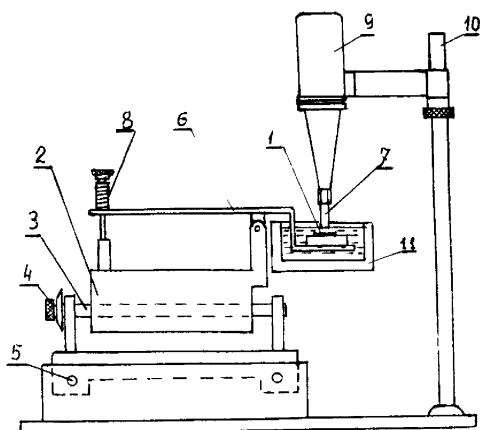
Схема устройства для поверхностной ультразвуковой обработки: 1-образец; 2-каретка; 3,5- направляющие для перемещения образца в двух взаимно перпендикулярных направлениях; 4-микро-винт с барабанной шкалой; 6-рычаг; 7-инструмент для ультразвуковой обработки поверхности; 8-пружина для поджима обрабатываемого образца к инструменту с заданным усилием; 9- магнито-стрикционный преобразователь; 10-стойка с платой для крепления магнито-стриктора и механизма перемещения образца; 11- емкость для жидкого азота
